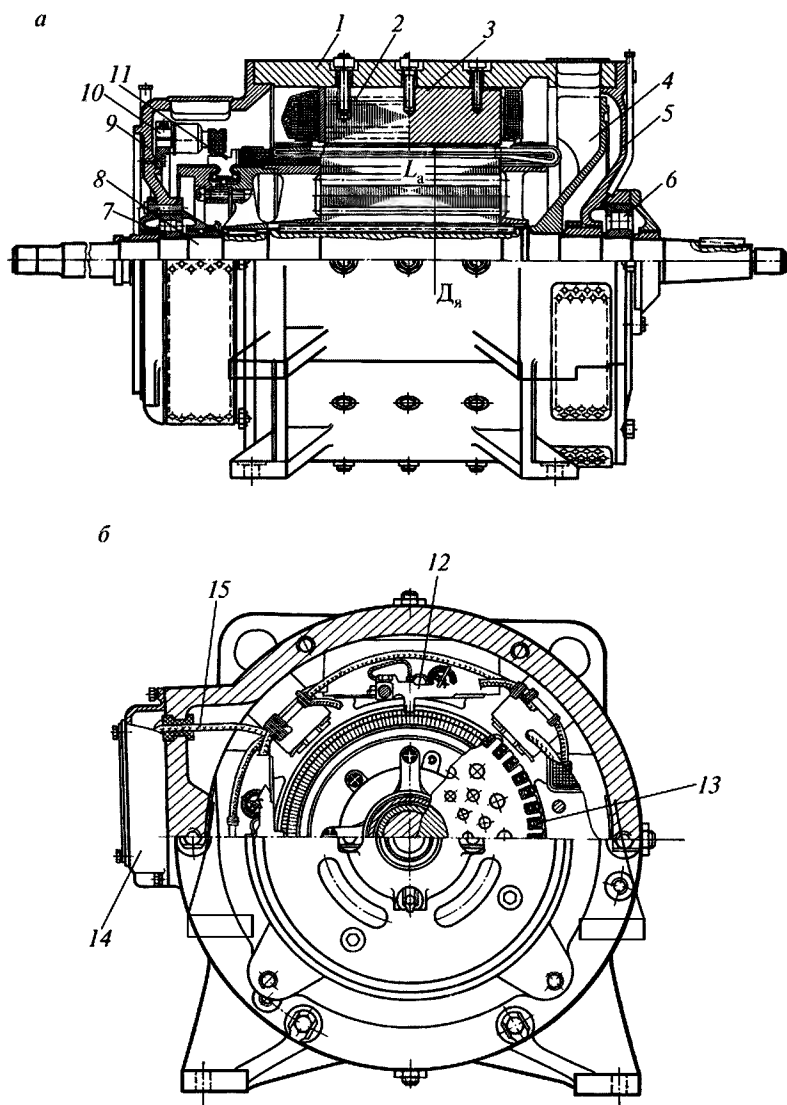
Продольный (а) и поперечный (б) разрезы двигателей НБ-430А:
